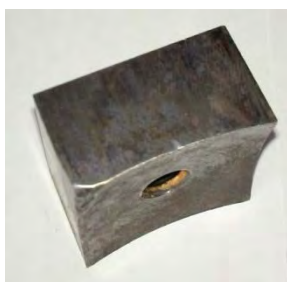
Опытный образец ножа для рубки щепы ФТИ5.001.1672
